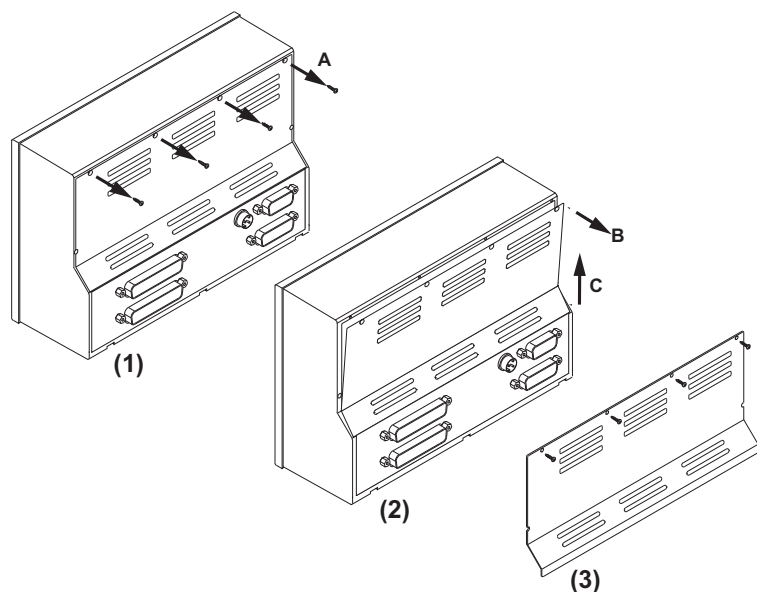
Entfernen des rückwärtigen Abdeckblechs
